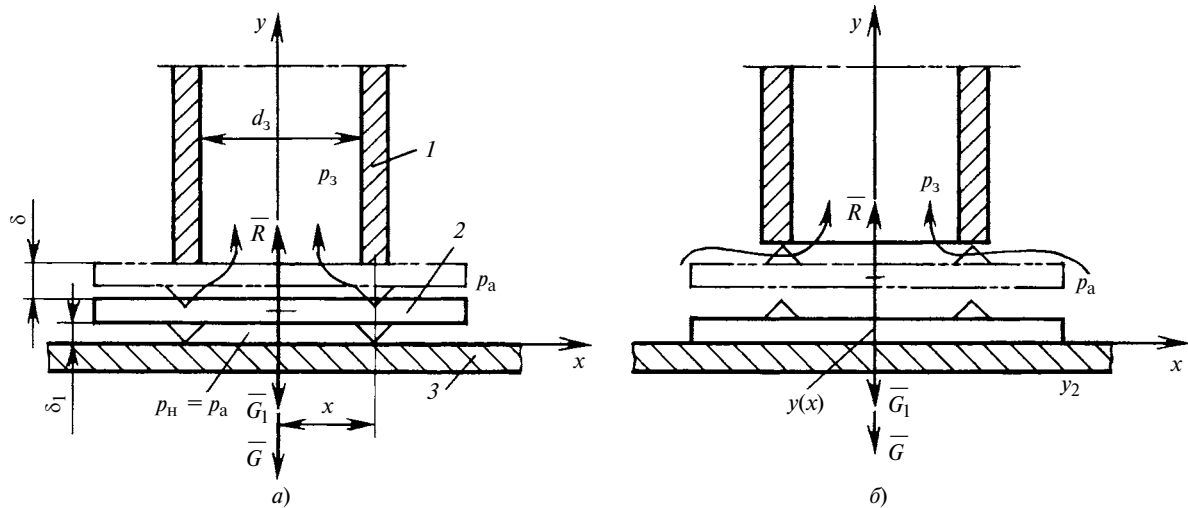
Схемы для определения основных параметров системы сортировки движущихся деталей с помощью вакуумного захвата: *a* — захват детали в положении пуклями вниз; *б* — незахват детали в положении пуклями вверх; *1* — вакуумный захват; *2* — деталь; *3* — лента транспортера
